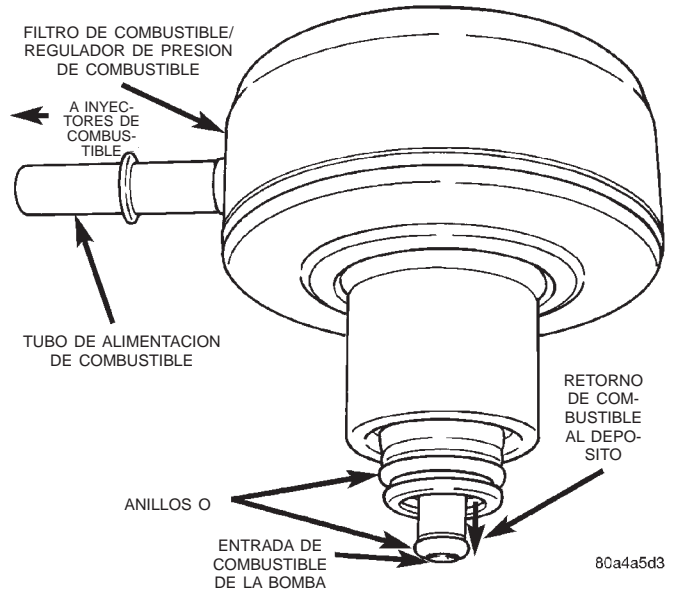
Anillos O del filtro de combustible/regulador de presión de combustible
